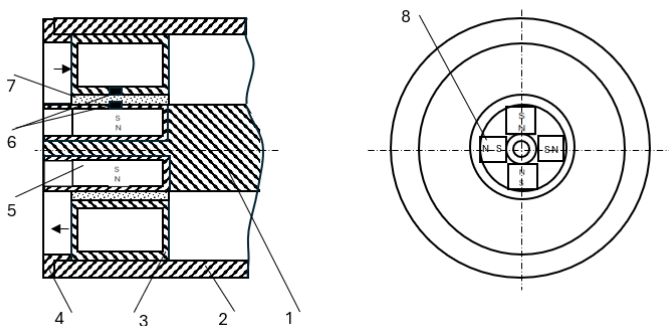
Схема магнитожидкостного подшипника скольжения (N-S) с магнитами на валу: 1 - немагнитный вал; 2 – корпус; 3,4,5 – втулки; 6 – термопары; 7 – магнитная жидкость с МУНТ; 8 – магниты
